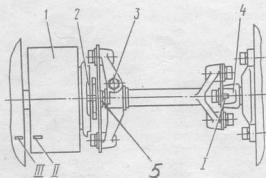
Установка начала впрыска топлива в 1-ом цилиндре двигателя по меткам:
